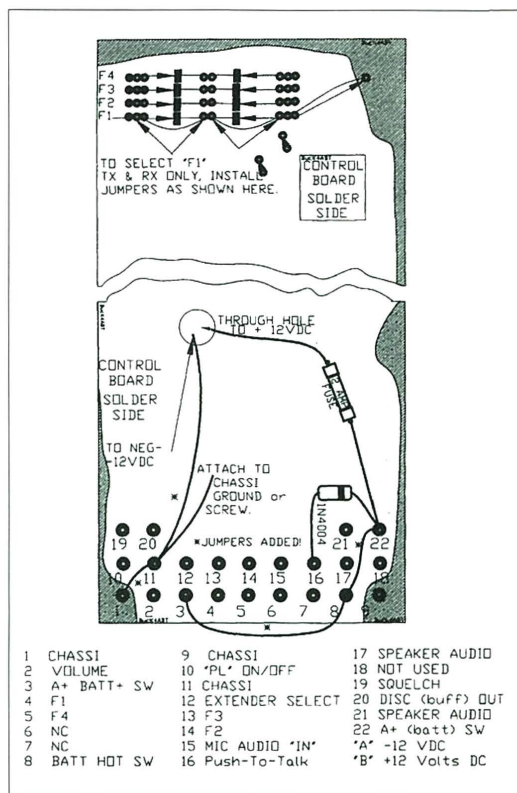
Lado de soldaduras de la unidad de control.
